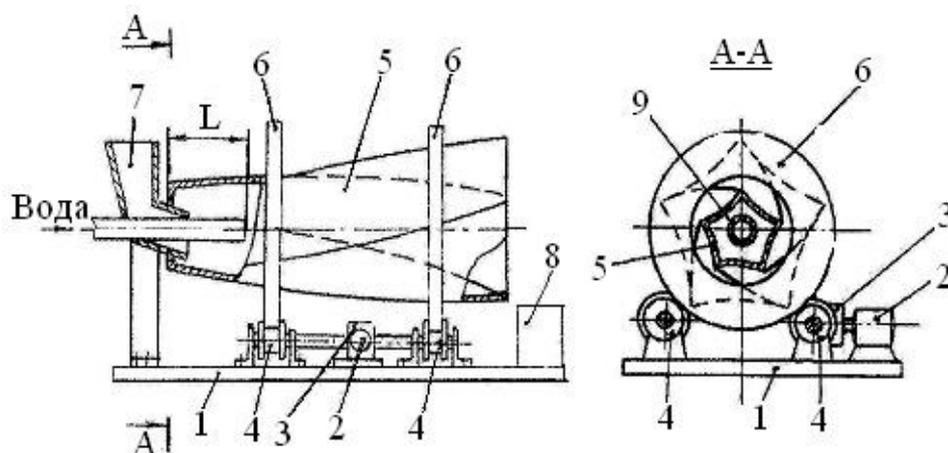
Бетоносмеситель (варианты) (1 – станина; 2 – электродвигатель; 3 – редуктор; 4 – четыре роликовые опоры; 5 – конусный барабан; 6 – два обода барабана; 7 – устройство для загрузки; 8 – устройство для выгрузки; 9 – трубопровод)
